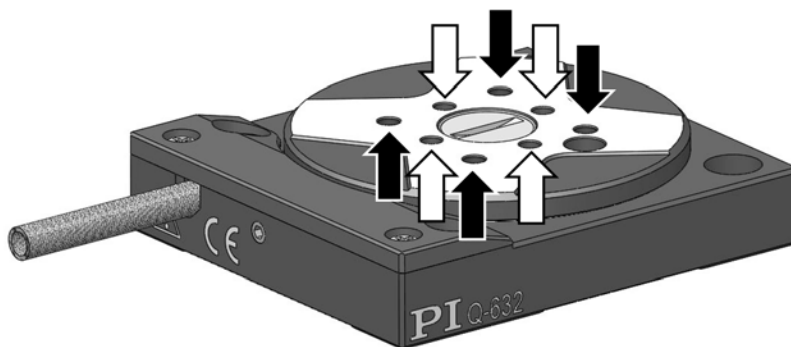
Schwarze Pfeile bezeichnen die Passbohrungen zum Ausrichten der Last, weiße Pfeile bezeichnen Gewindebohrungen zum Befestigen der Last
